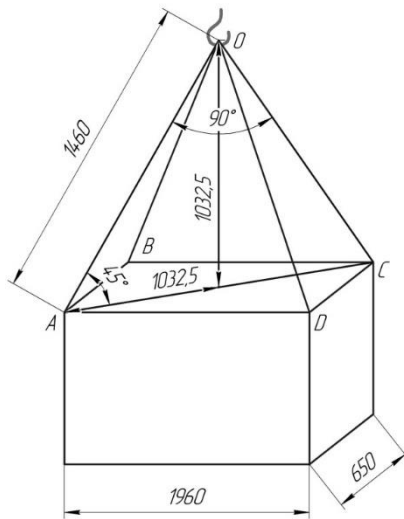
Схема строповки редуктора ЦДН – 630
